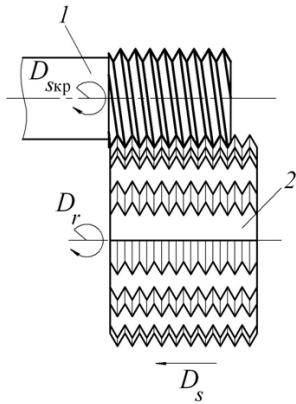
Схема фрезерования резьбы многозубчатой гребенчатой фрезой: 1 – заготовка; 2 – фреза
